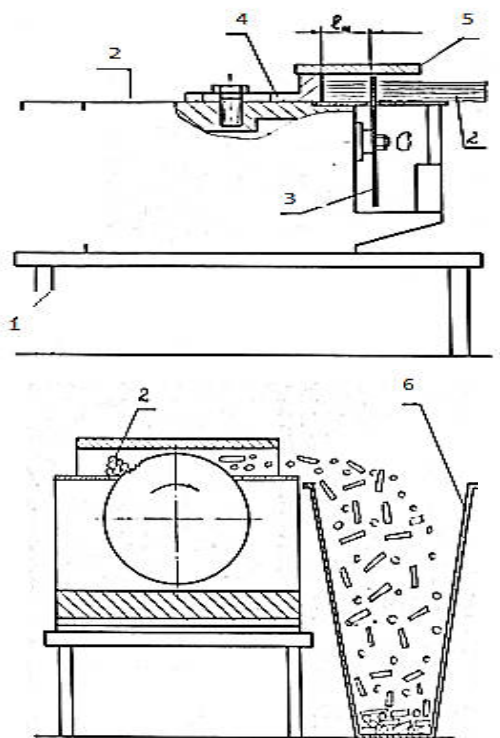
Схематичное изображение установки для получения щепы из обрезной древесины
